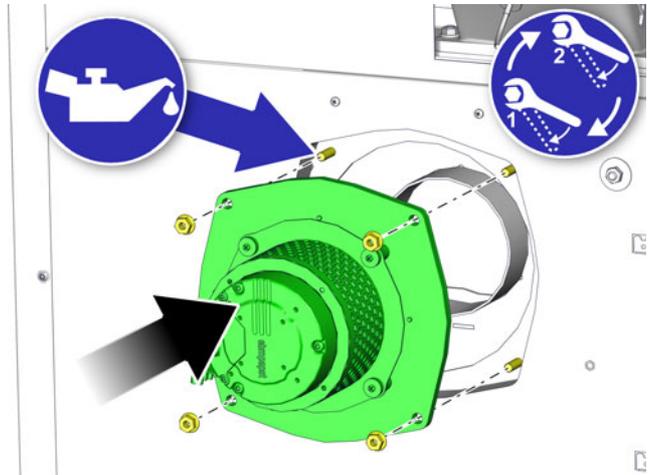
Nettoyage du rotor et remplacement du joint
